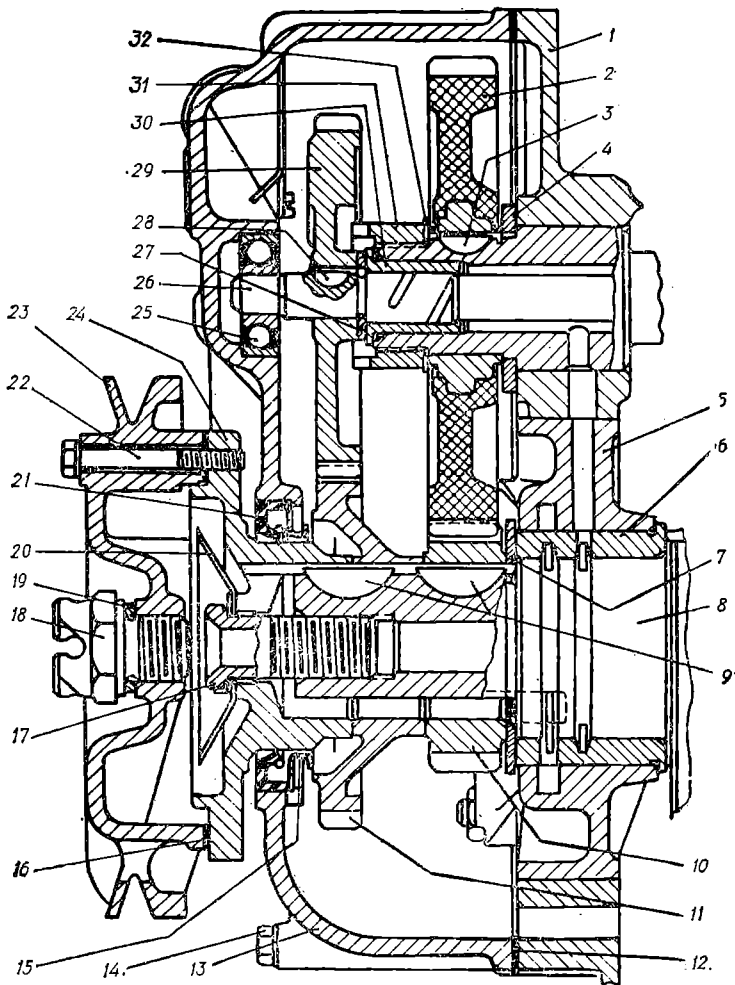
Центробежный маслоочиститель, передний коренной подшипник и привод распределительного вала и балансирующего механизма:
